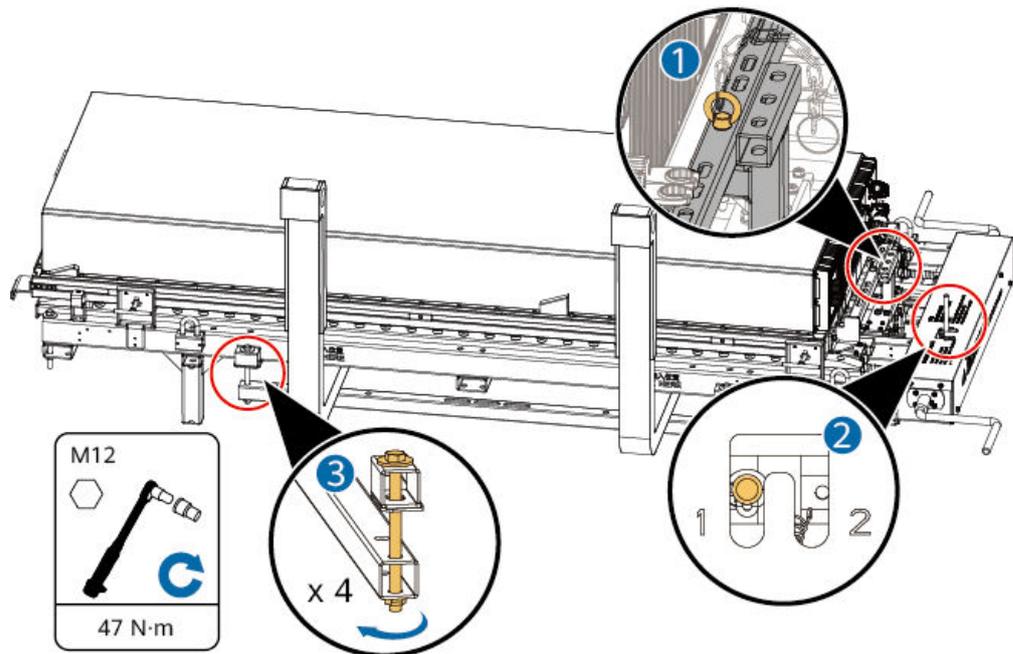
Cómo poner la batería sobre el dispositivo auxiliar
